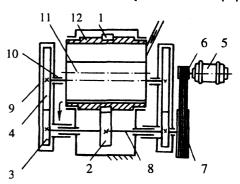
Схема головки ролико-кольцевой мельницы с саморегулируемым режимом размола: 1 – зубчатое колесо кольца; 2, 3 – зубчатые колеса вала-шестерни; 4 – зубчатые колеса валка; 5 – электродвигатель; 6, 7 – ведущий и ведомый шкивы клиноременной передачи; 8 – ведущий вал-шестерня; 9 – серьги; 11 – валок; 12 – кольцо
